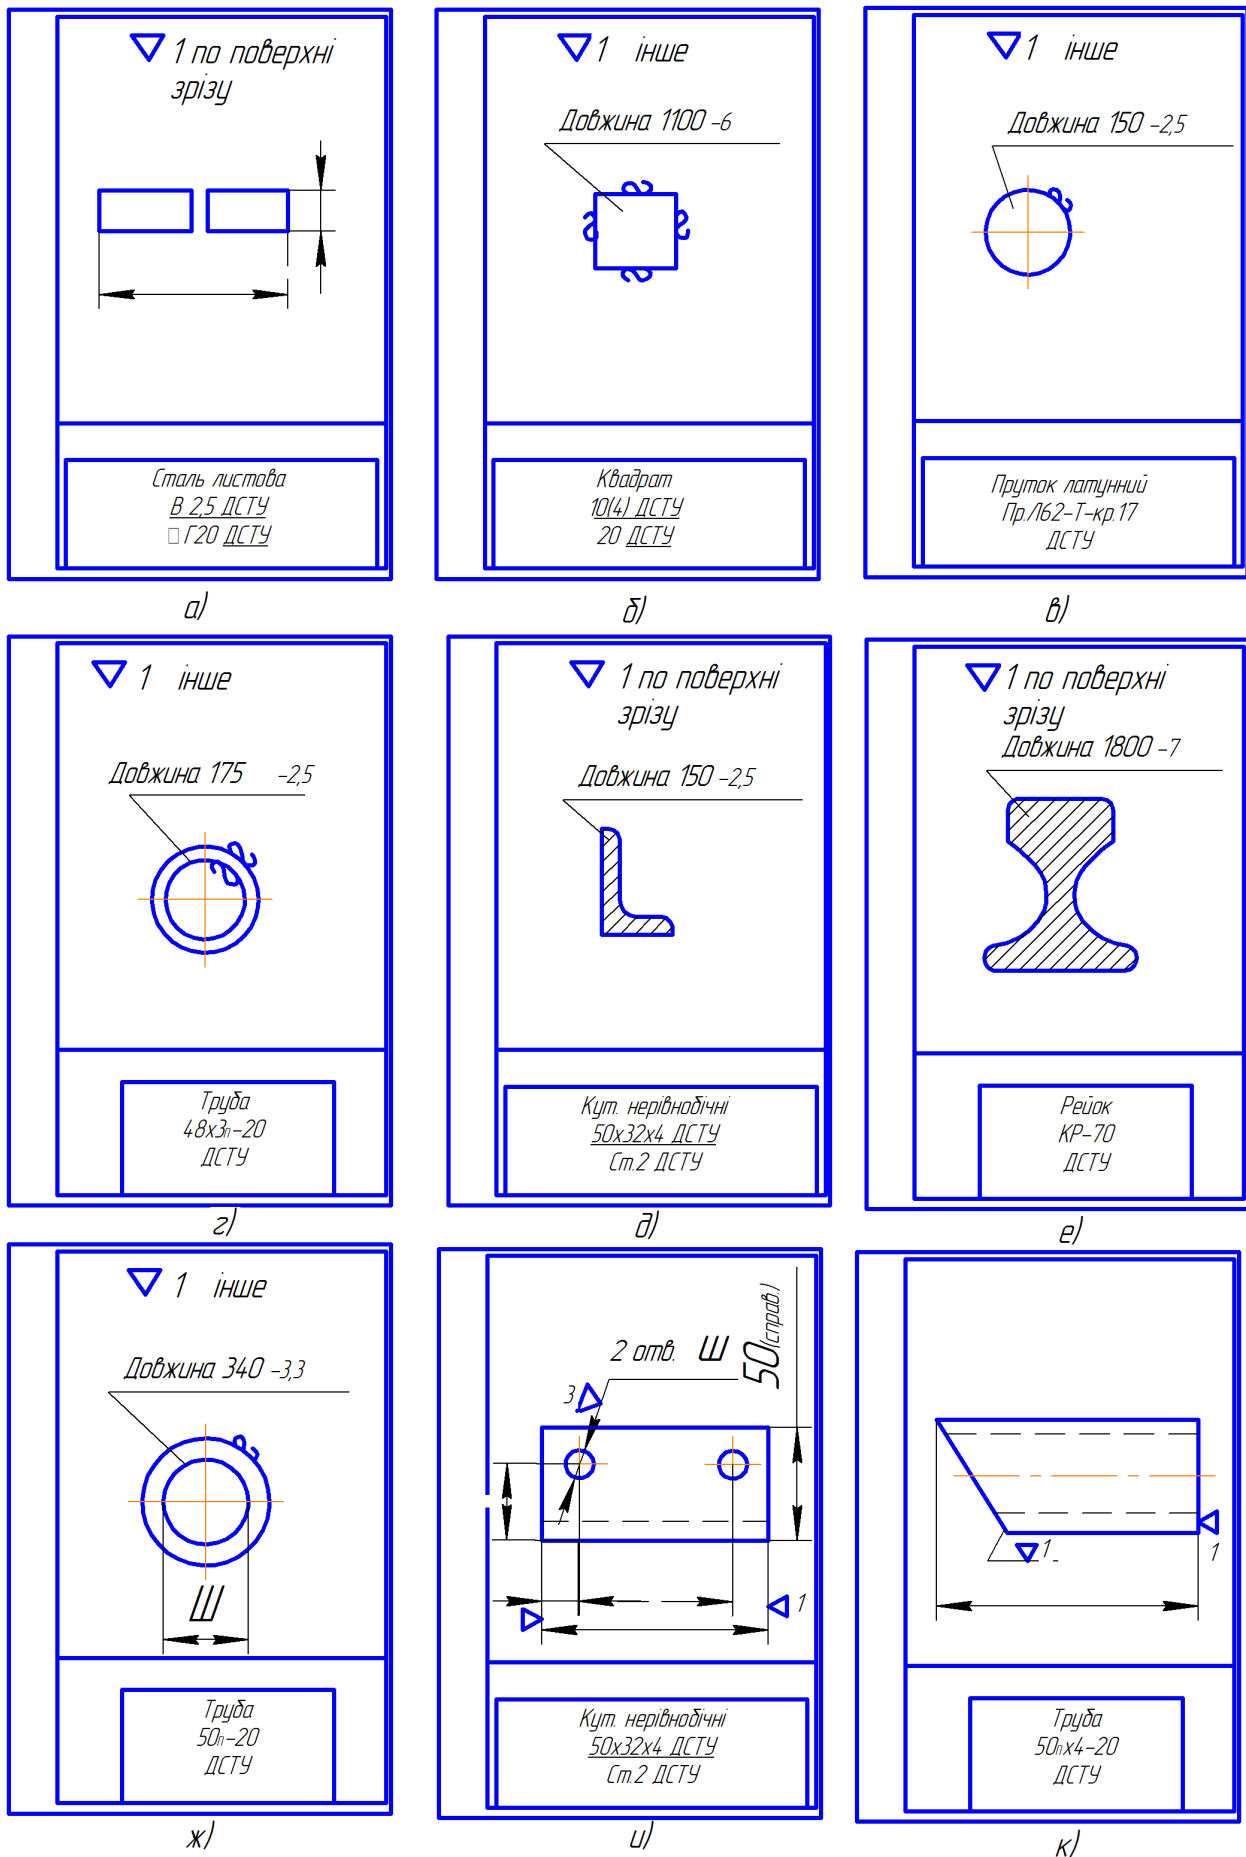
Приклади креслень деталей із сортового прокату
